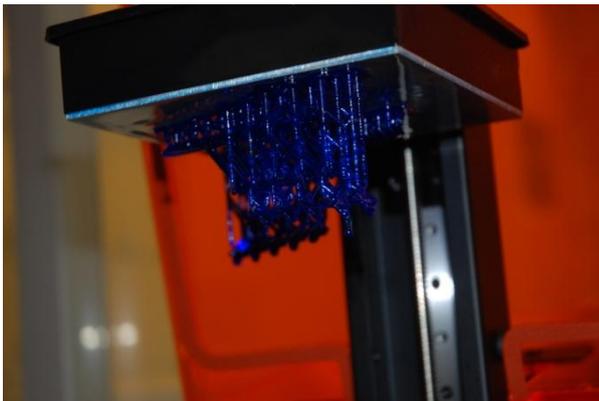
Vue d'ensemble de la zone prototypage rapide
